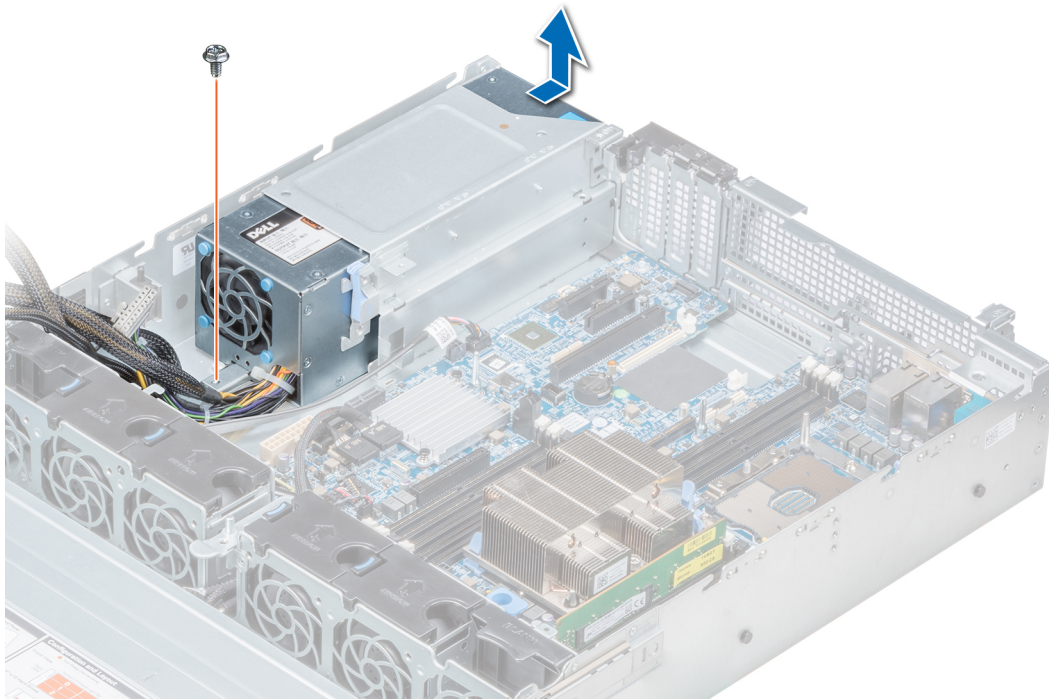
Desmontaje de una PSU de CA no redundante con cable
